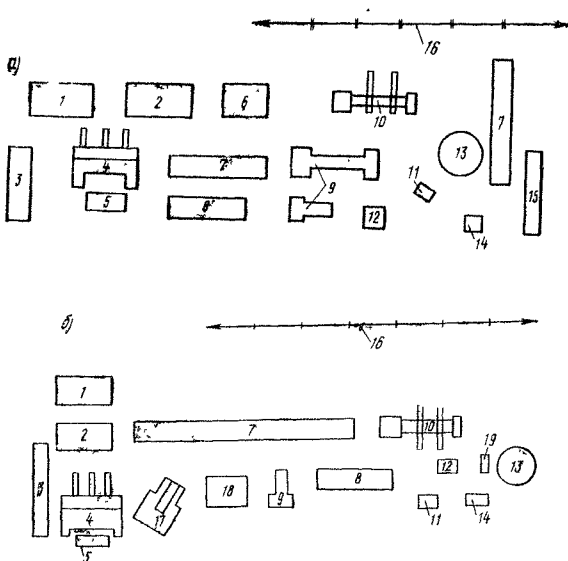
Типовая технологическая планировка участка изготовления сварных воздуховодов круглого и прямоугольного сечений
